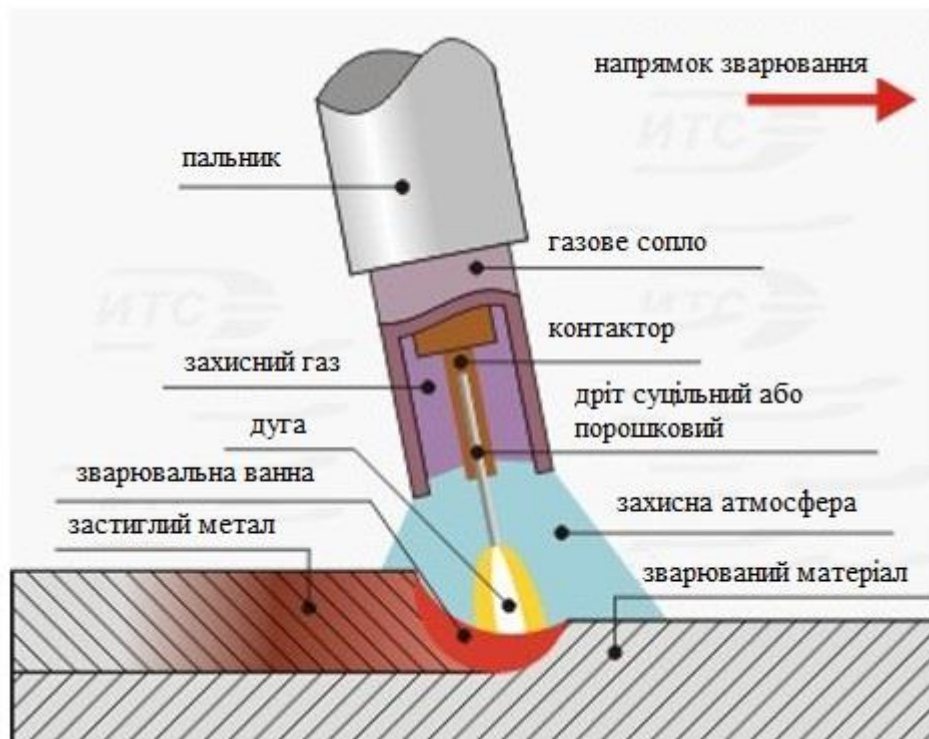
Схема механізованого зварювання в середовищі захисних газів
